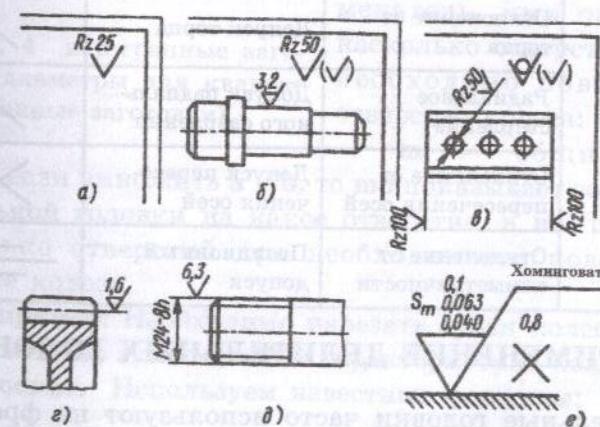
Обозначение шероховатости поверхности (по О'з DST 646-95).
